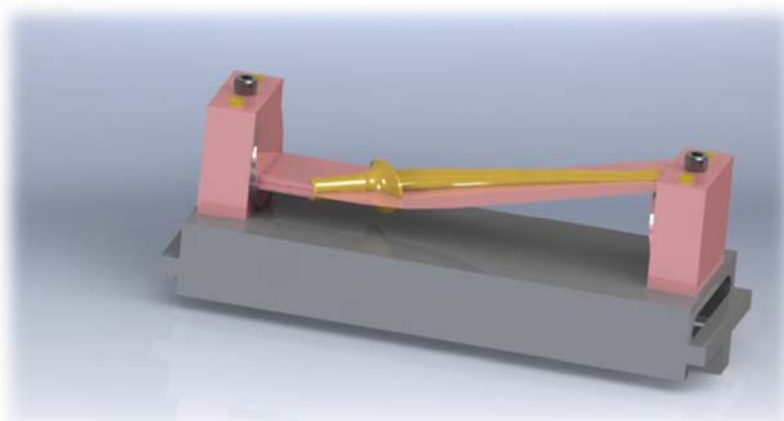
Posicionamento da prótese para a primeira etapa de maquinagem e superfície que define a altura máxima de maquinagem.
